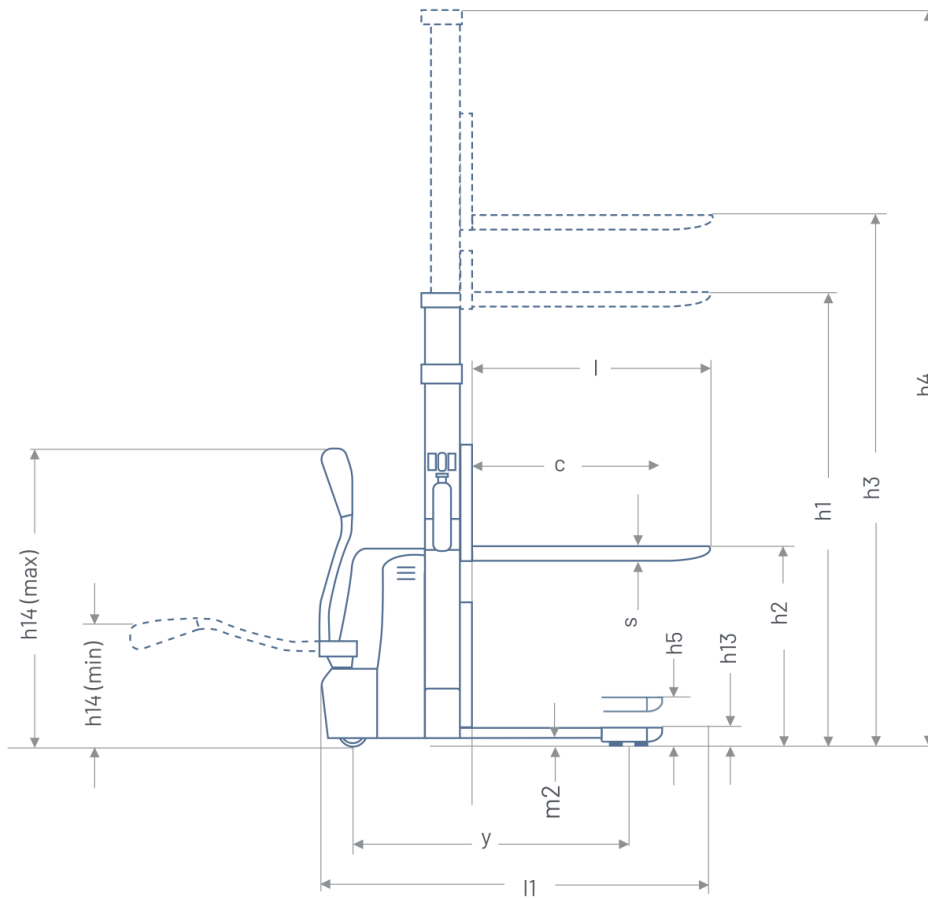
Seitenansicht des DOUBLE-S mit Kürzeln
